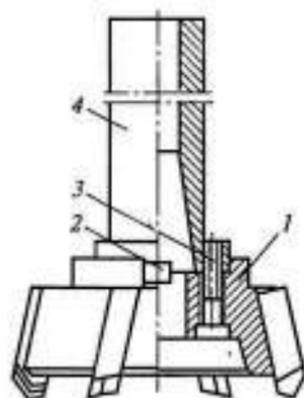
Установка торцовых насадных фрез на шпиндель станка:
